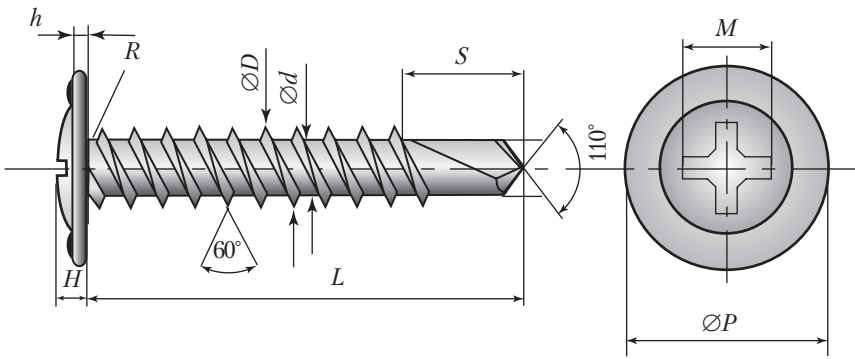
Саморіз для металу з прес-шайбою та свердлом
